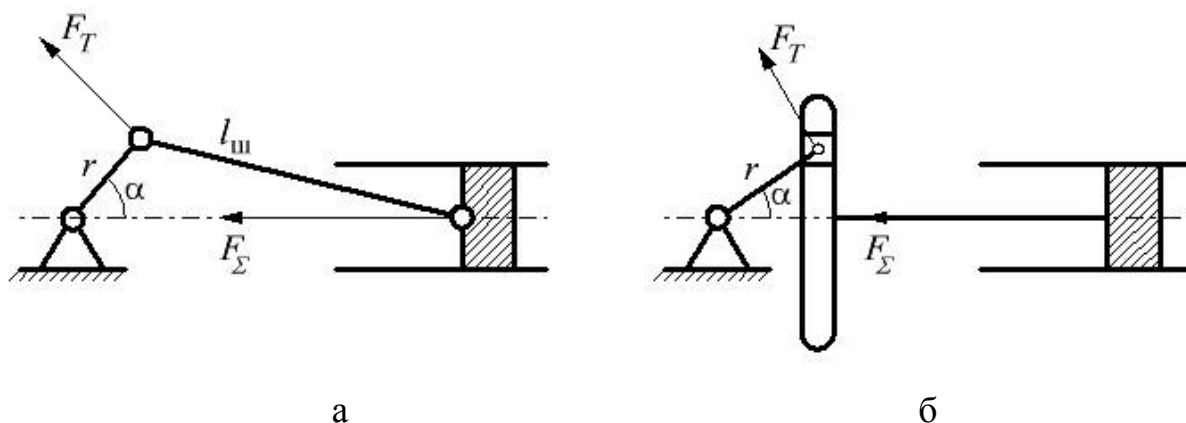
Кінематична схема кривошипного механізму компресора:
